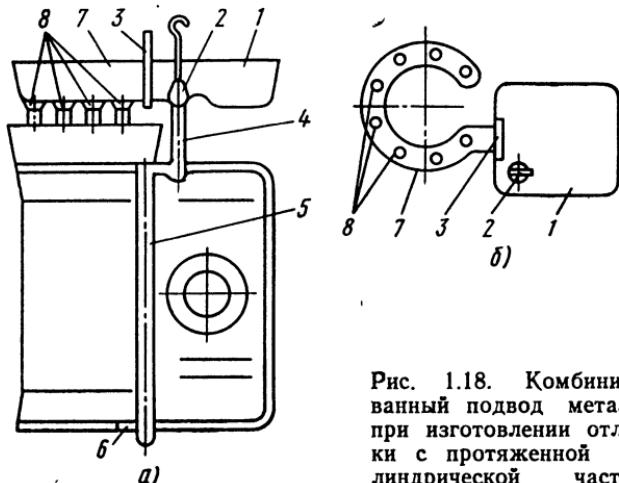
Комбинированный подвод металла при изготовлении отливки с протяженной цилиндрической частью:
